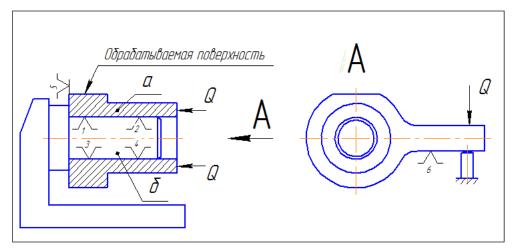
Схема установки заготовки с базой по внутренней цилиндрической поверхности
